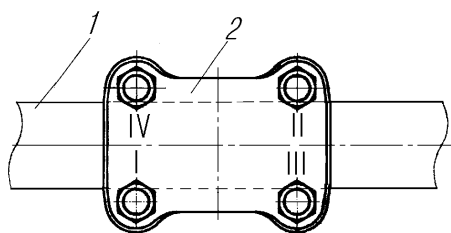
Схема затяжки гаек стремянок рессор: 1-рессора; 2-балансир задней рессоры (балка переднего моста); I-IV-порядок затяжки гаек стремянок
